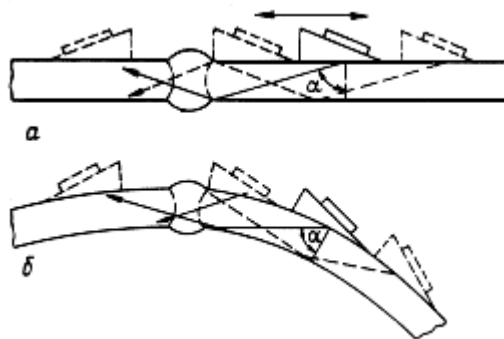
Схема ультразвукового контроля сварных соединений реакторов: а - кольцевых соединений; б - продольных соединений
